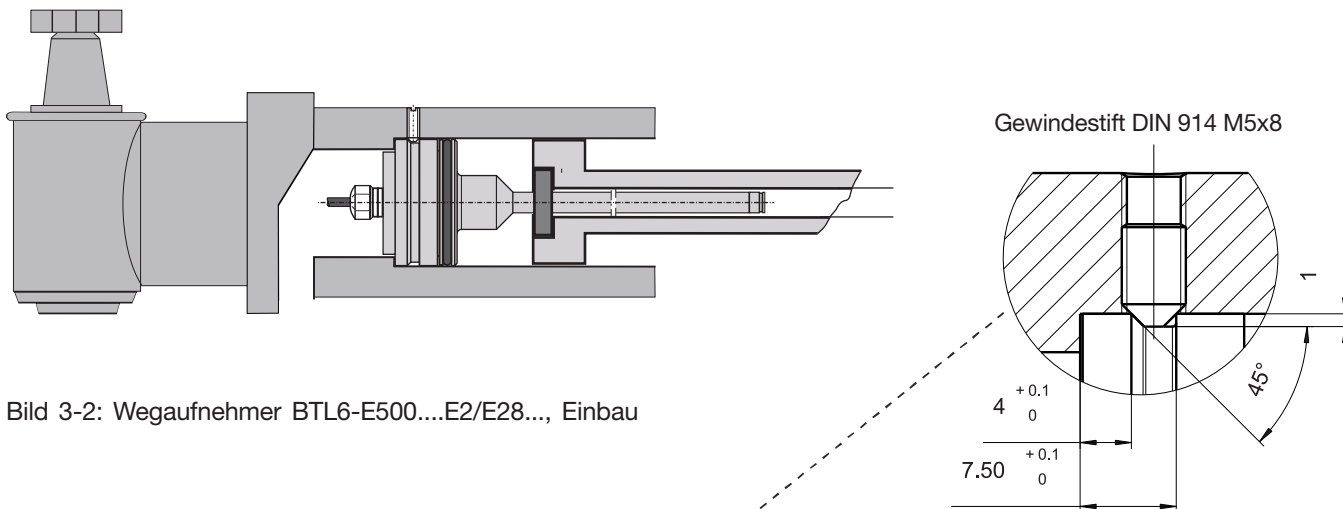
Wegaufnehmer BTL6-E500....E2/E28..., Einbau
